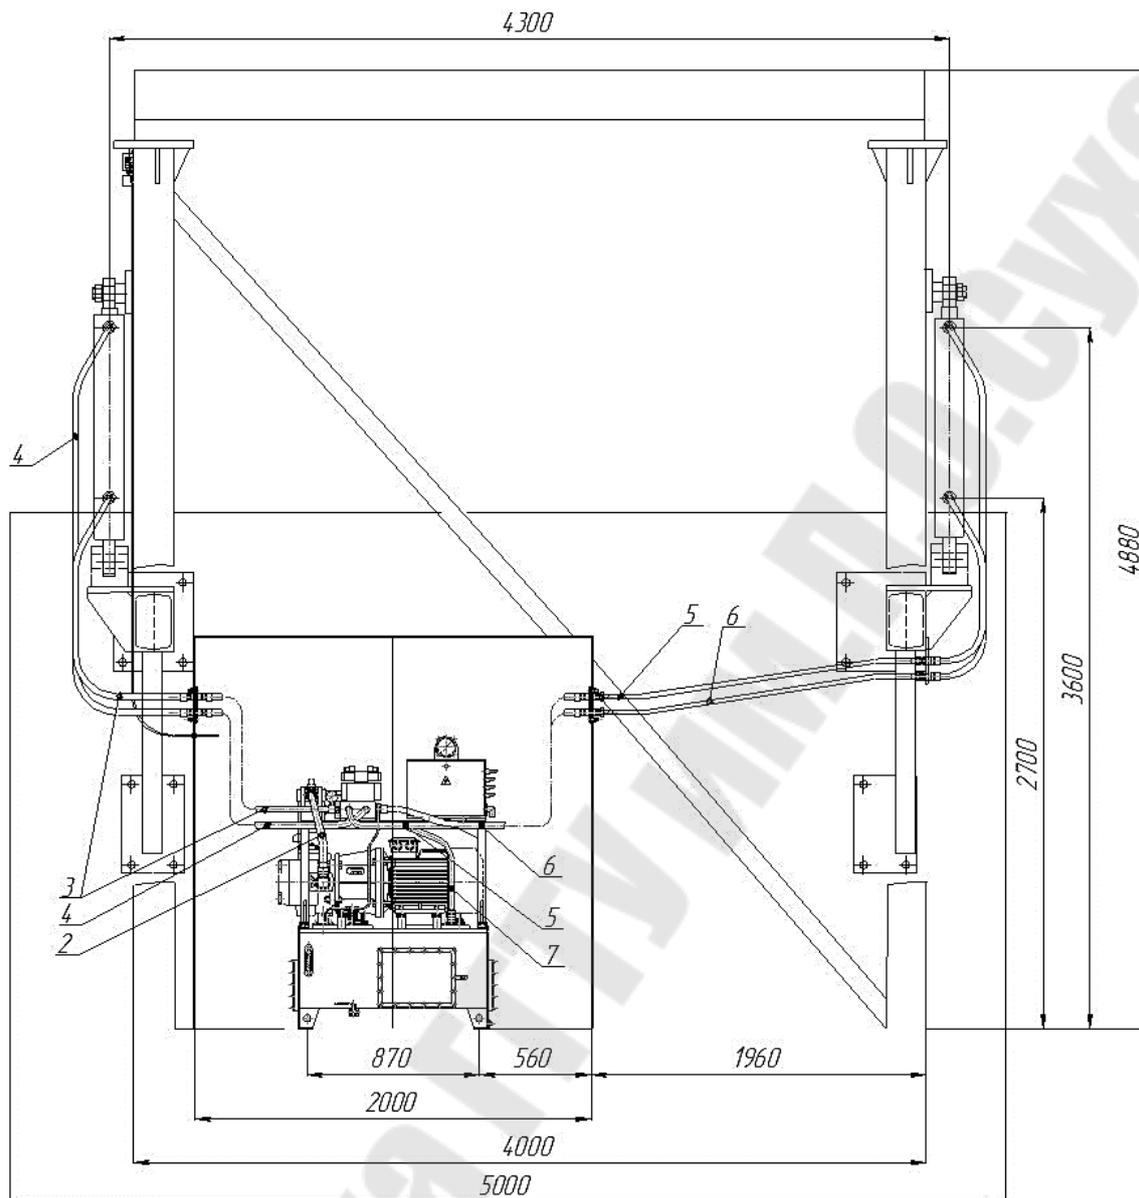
Монтажная схема трубопроводов на линии переработки шлака (вид спереди)
